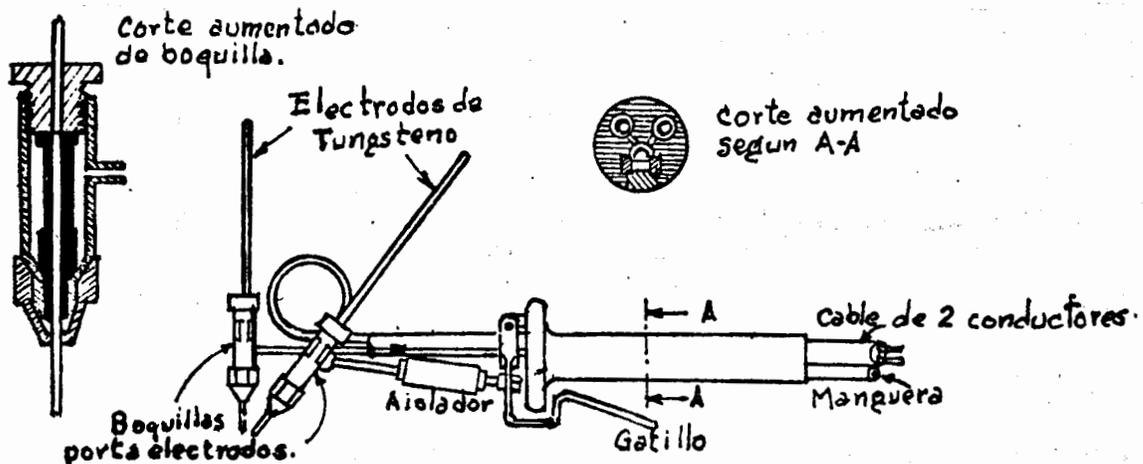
SOPLETE PARA SOLDADURA DE ARCO CON HIDROGENO ATOMICO.
